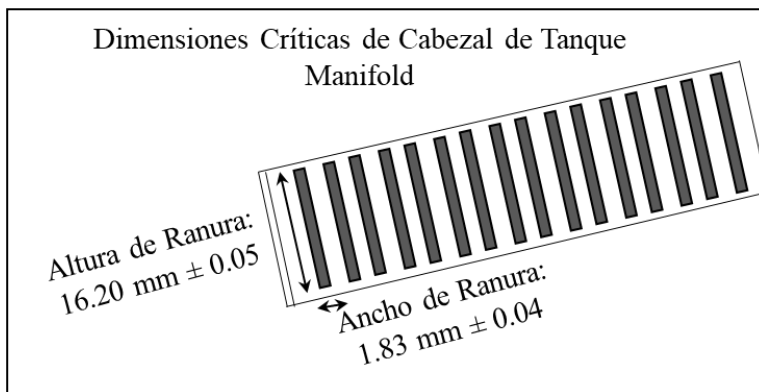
Dimensiones críticas de cabezal de tanque manifold
